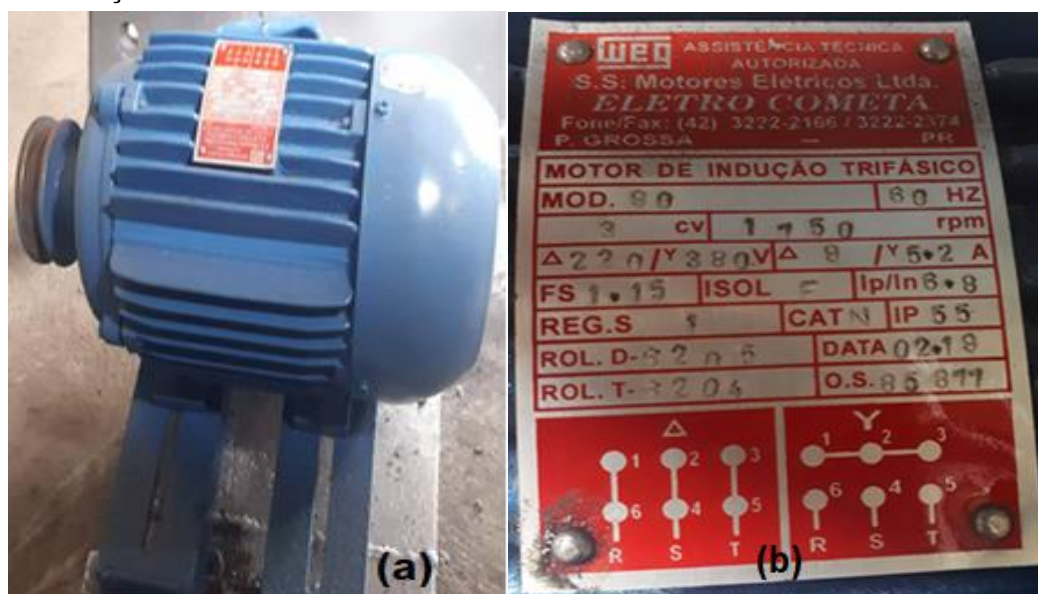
Motor utilizado na Calandra – a) vista frontal; b) vista superior
